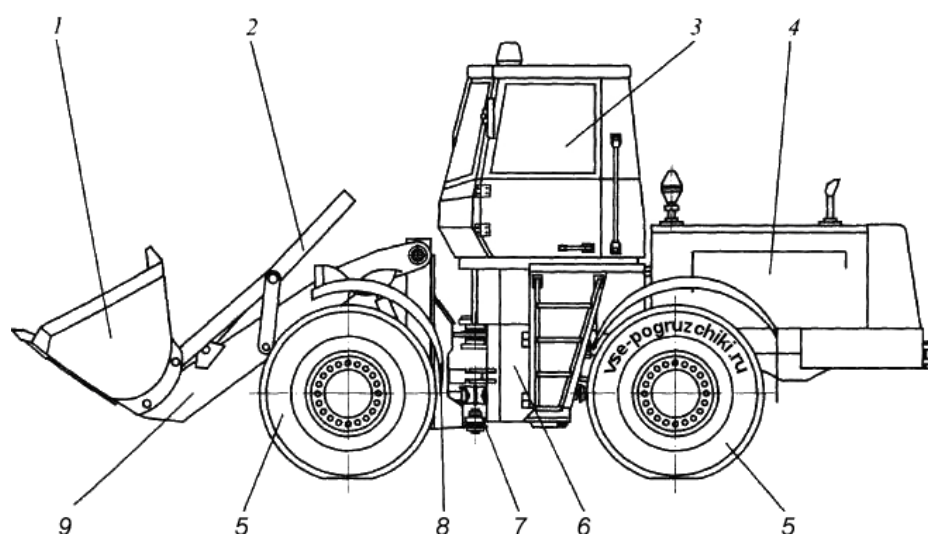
Схема фронтального погрузчика: 1 – ковш; 2 – гидроцилиндры управления ковшом; 3 – кабина оператора; 4 – двигатель; 5 – пневмоколеса; 6 – задняя рама; 7 – шарнирное сочленение рам; 8 – передняя рама; 9 – стрела
